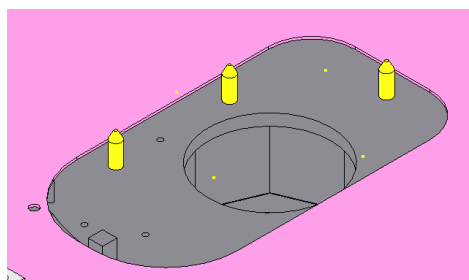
Finální svařovací přípravek pro součást 5150
